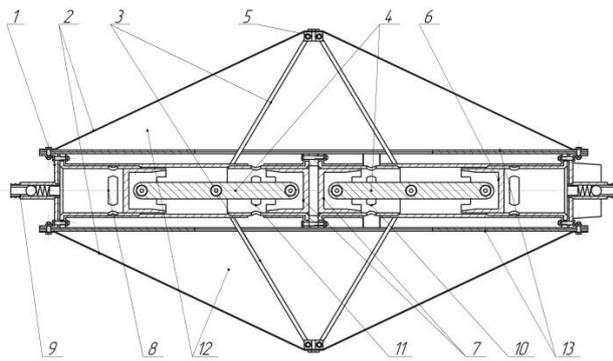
Вид сбоку (разрез в плоскости симметрии): 1 – корпус свободнопоршневого привода; 2 – мембраны; 3 – механизм синхронизации; 4 – поршневые группы; 5 – крепление мембраны к механизму синхронизации; 6 – буферные поршни; 7 – рабочие поршни; 8 – буферные цилиндры; 9 – пусковые клапаны; 10 – заборные полости; 11 – выпускные окна; 12 – подмембранное пространство; 13 – основание
